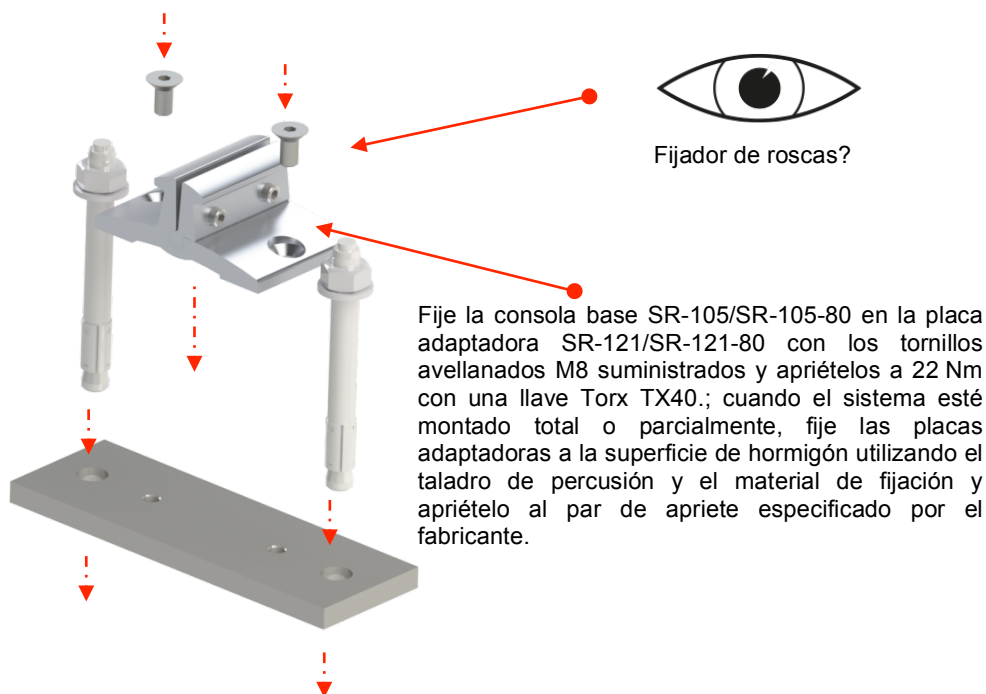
Montaje de la consola básica SR-105 en la placa adaptadora SR-121/SR-121-80
